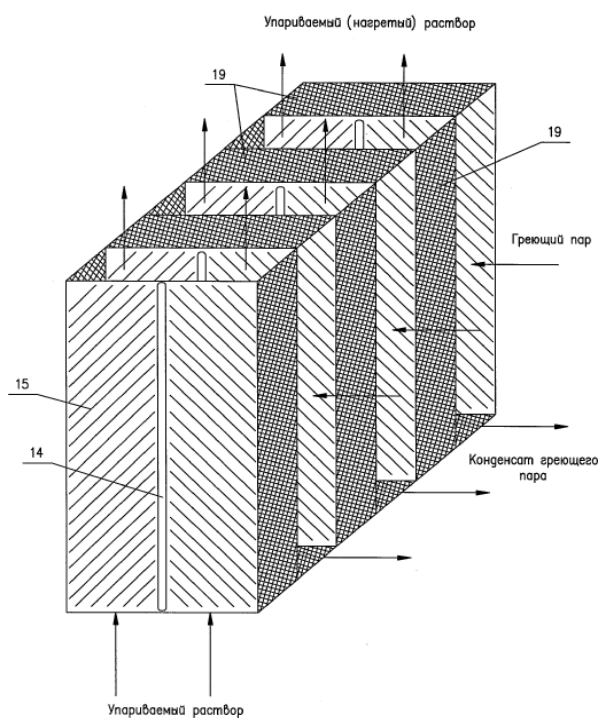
Компоновка пластин сварной греющей камеры
